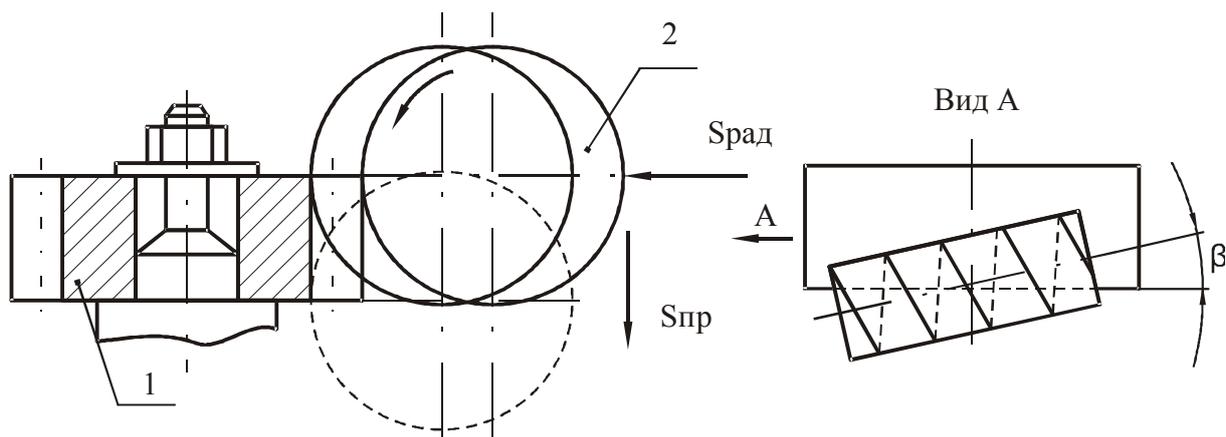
Схема фрезерования зубьев червячной фрезой
